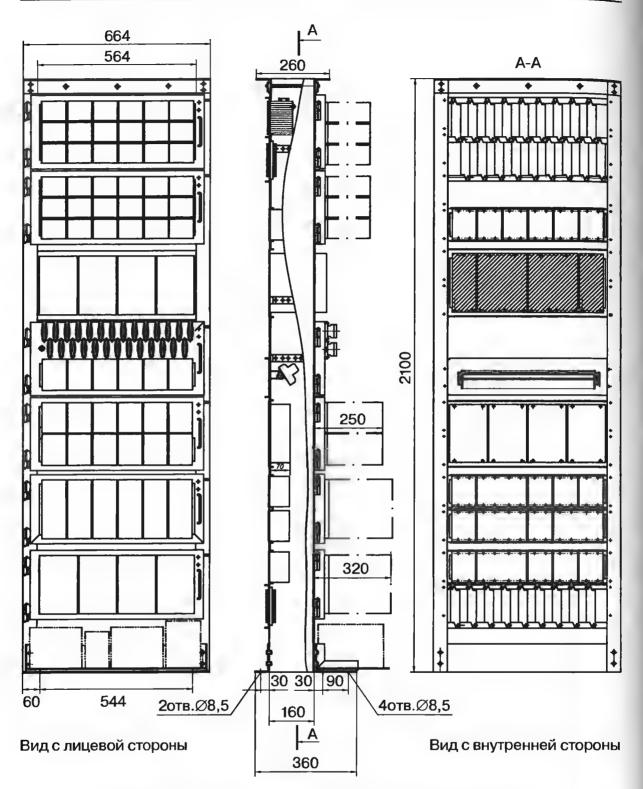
Статив пристенный СУР2-П, черт. 561-00-00
